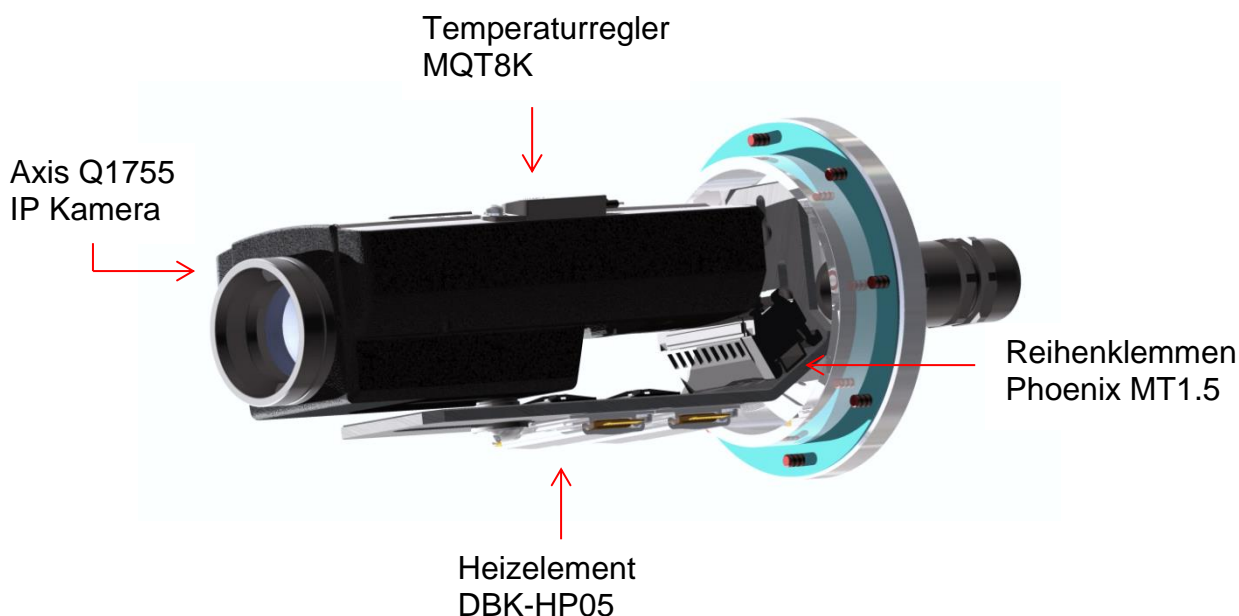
ExCam IPQ1755 Einbaukomponenten
